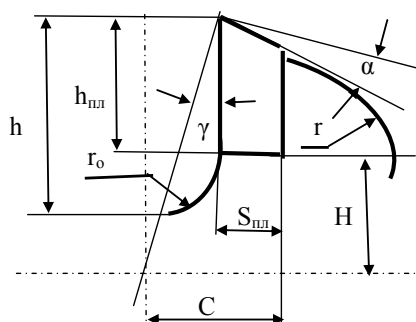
Профиль торцового сечения фрез с напайными пластинками винтовой формы: r_0 – радиус дна стружечной канавки; r – радиус спинки зуба
